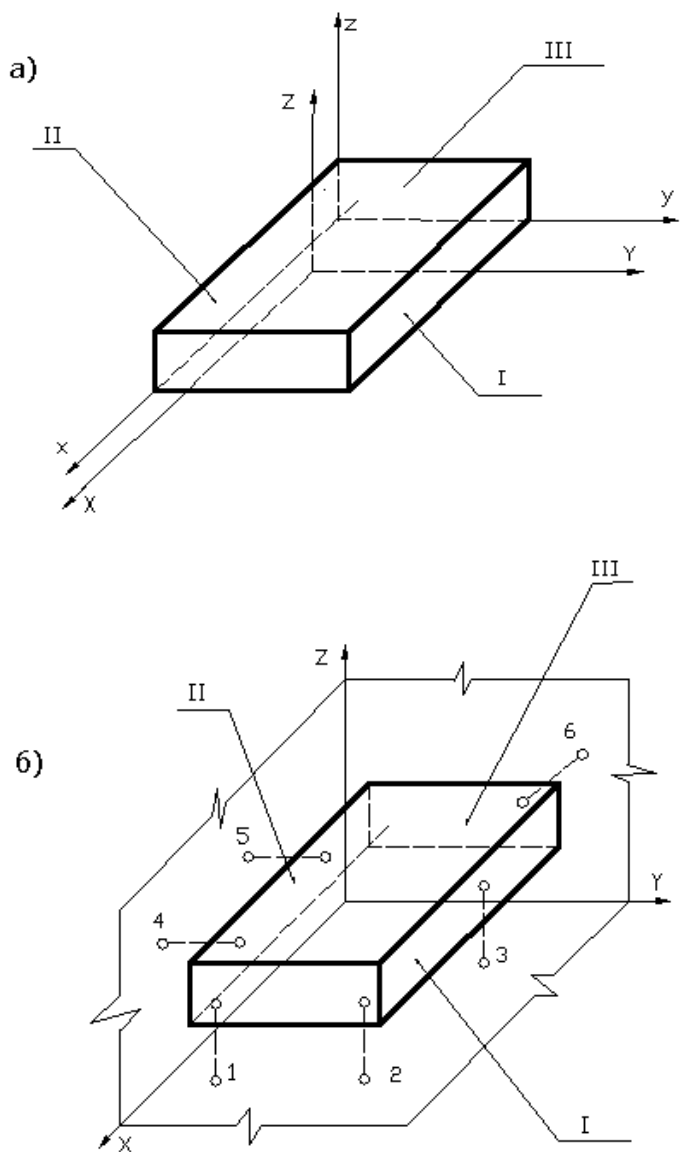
Комплект баз (а) и опорные точки (б) при базировании призматической заготовки (детали):
